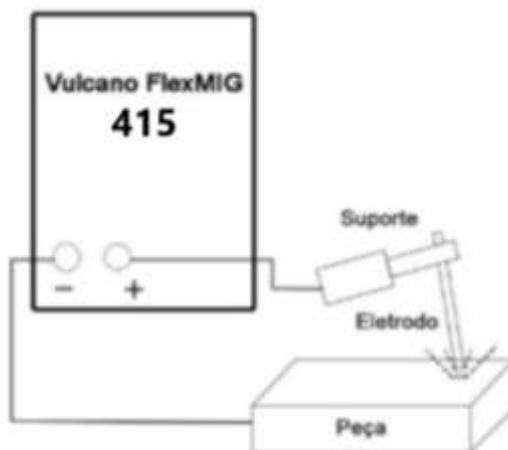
Conexão negativa para soldagem com eletrodo revestido.
